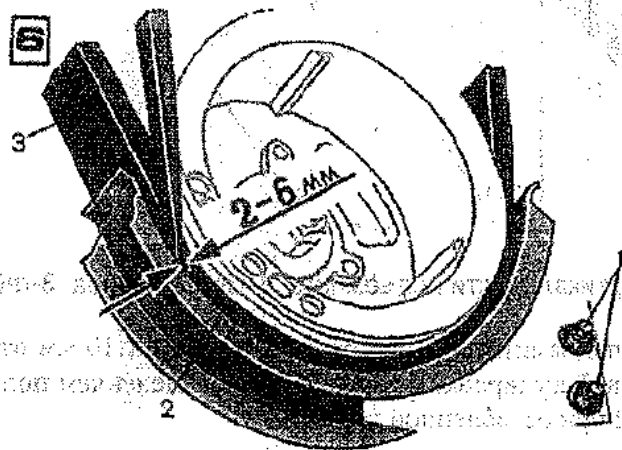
Схема регулировки зазора между нижним кожухом и ремнем: 1 - болты; 2 - кожух; 3 - ремень
